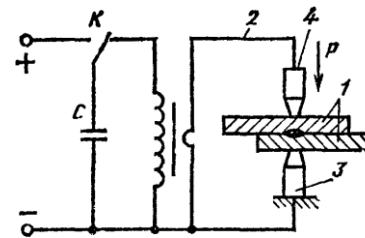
Схема конденсаторной сварки
